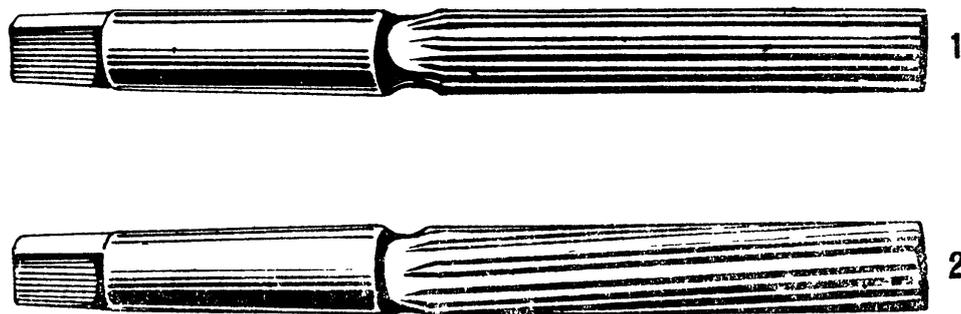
Цилиндрические развертки: 1—с прямыми ребрами; 2 — со спиральными ребрами
